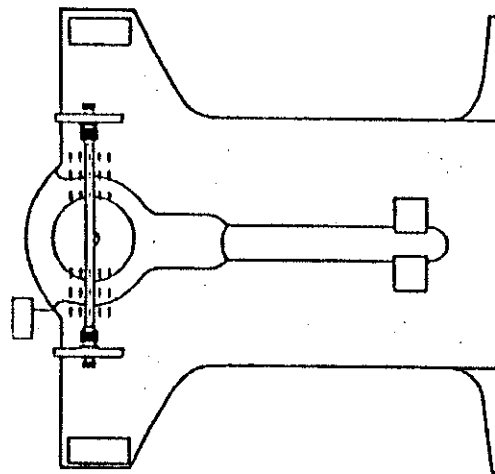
Контроль сварного соединенне нижнего листа с пятниковой отливкой
